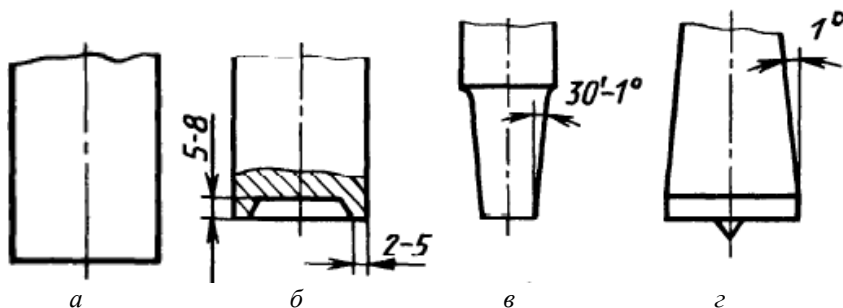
Формы рабочей части пуансонов для пробивки и вырубki
